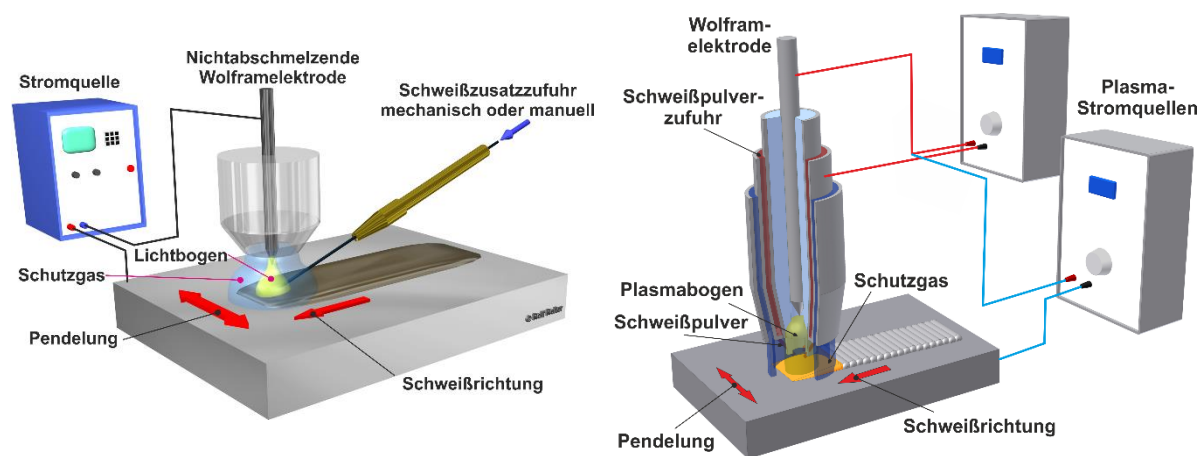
Verfahren für das Auftragschweißen an Extruderschnecken: links: WIG-Auftragschweißen, rechts: PPA-Schweißen (Bilder: R. Reiter)
